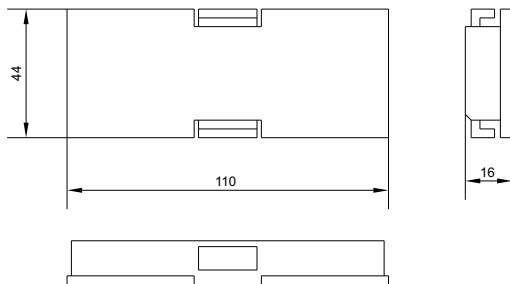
Внешний вид заглушки для универсальной панели / Figure 3 – Appearance of the plug for the multi-purpose panel /
